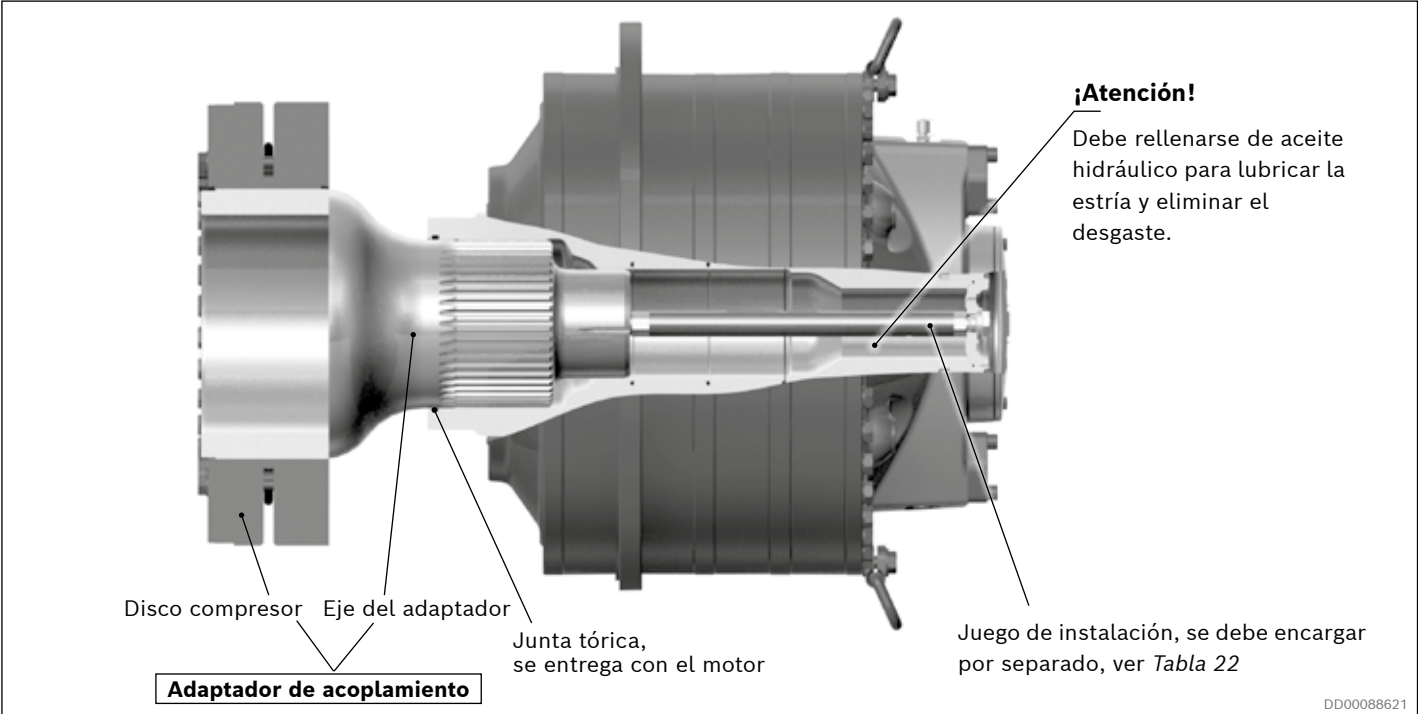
Motor CB 1120 con adaptador de acoplamiento
